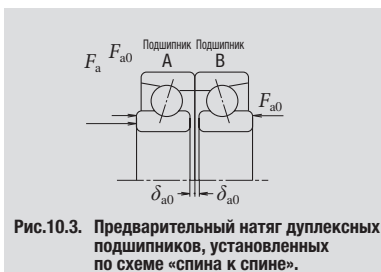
Предварительный натяг дуплексных подшипников, установленных по схеме «спина к спине».
